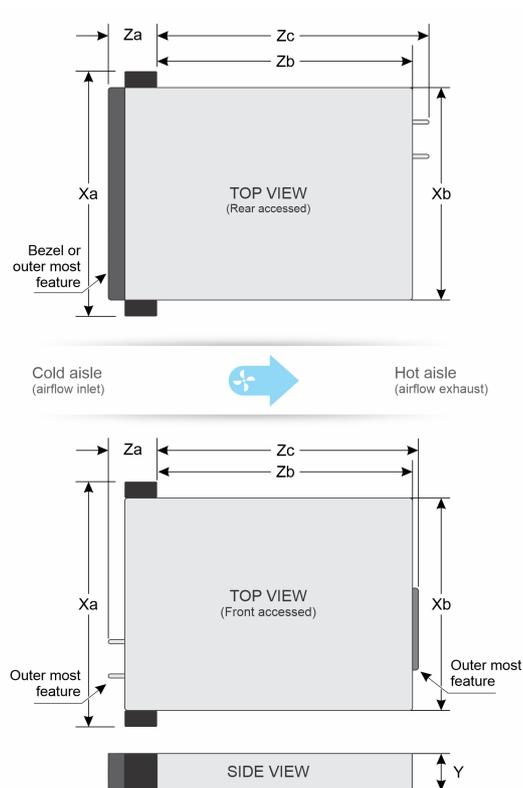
Dimensions du châssis XR11 avec accès par l'arrière (haut) et accès par l'avant (bas)
